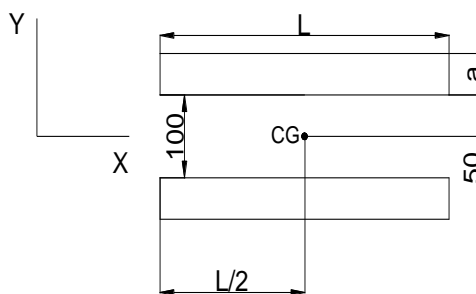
3: Abatimiento de los cordones de soldadura
